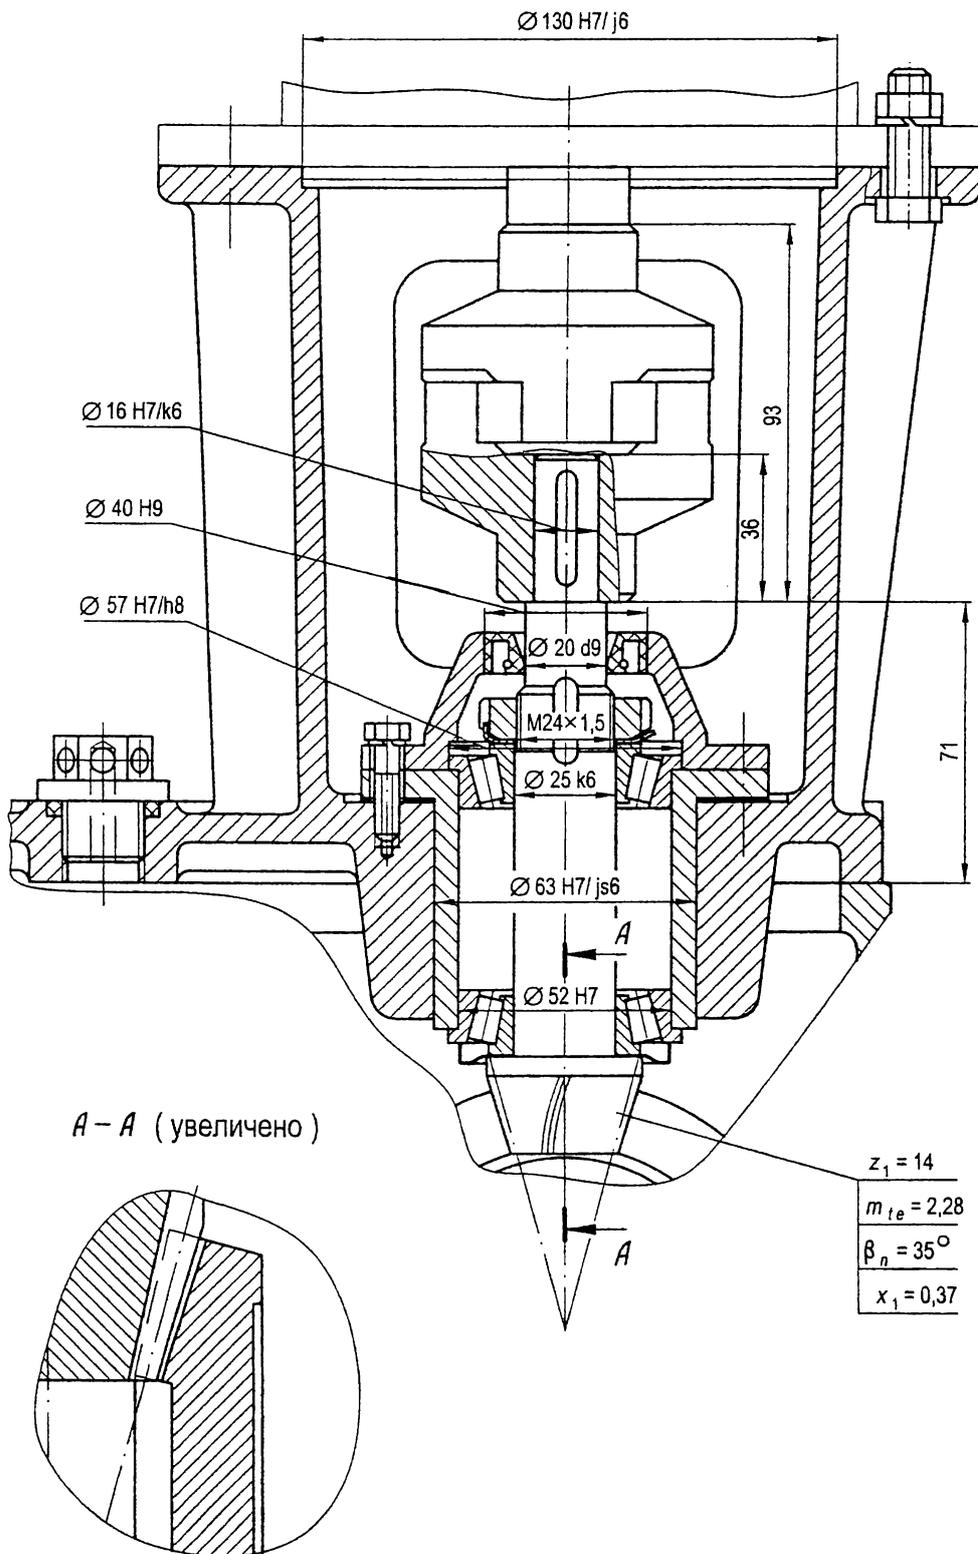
Вал конической шестерни с вертикальной осью вращения (быстроходный вал коническо – цилиндрического мотор – редуктора)
